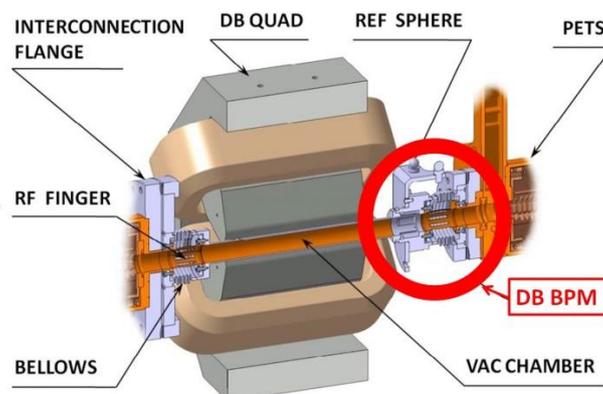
Detalle del emplazamiento de los BPMs en el “Drive Beam”.
